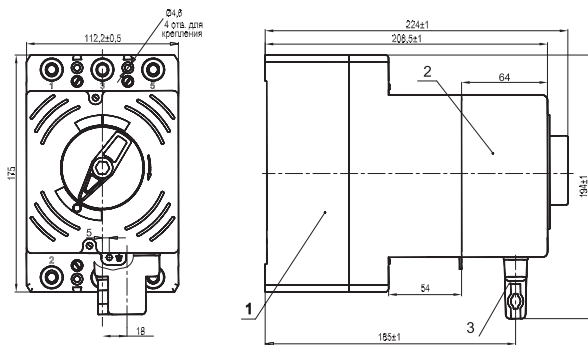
Расположение отверстий для крепления выключателя
